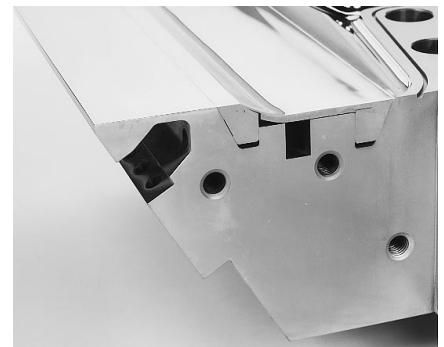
Ausschnitt einer Werkzeughälfte mit integrierter Membran („Flexible Preland“). Das den Fließkanal bildende 1,5 mm dicke Federstahlblech ist fest auf zwei Profilleisten aufgeschweißt. Die gesamte in die Werkzeughälfte eingeschraubte Membraneinheit kann, wenn erforderlich, schnell ausgetauscht werden
